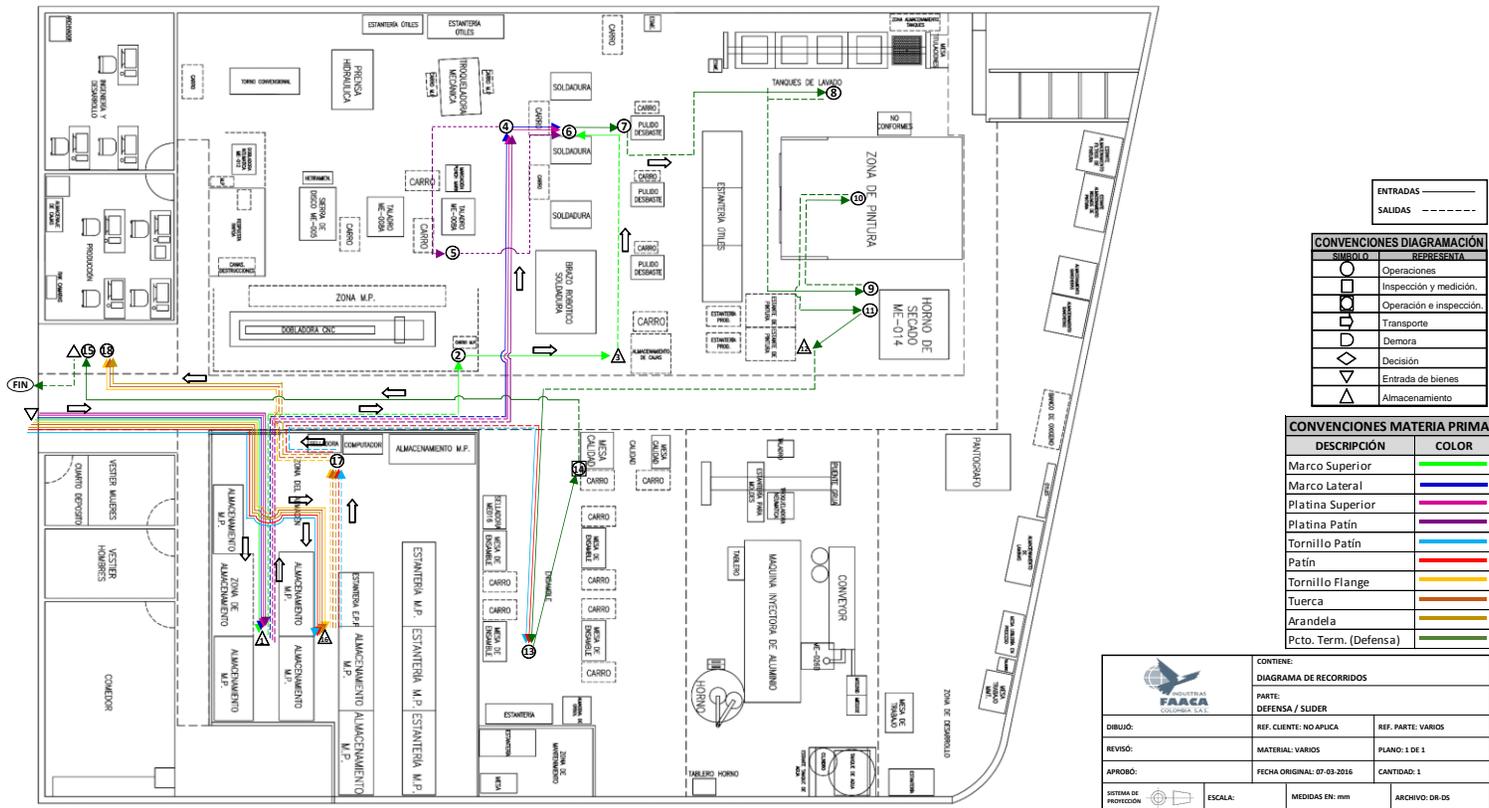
Diagrama de recorrido planta N° 2 – Parrillas.
